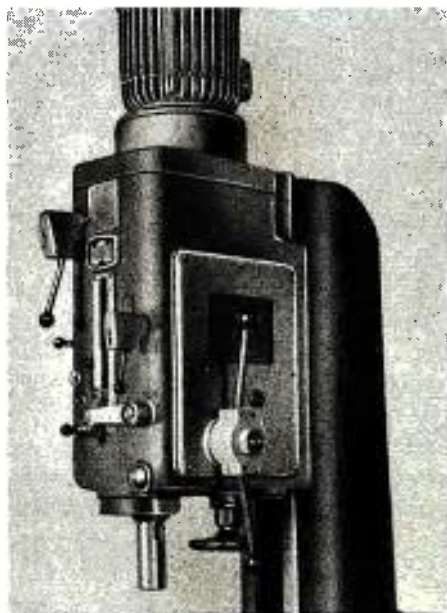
/1 Drehstrommotor zum Antrieb einer Werkzeugmaschine
